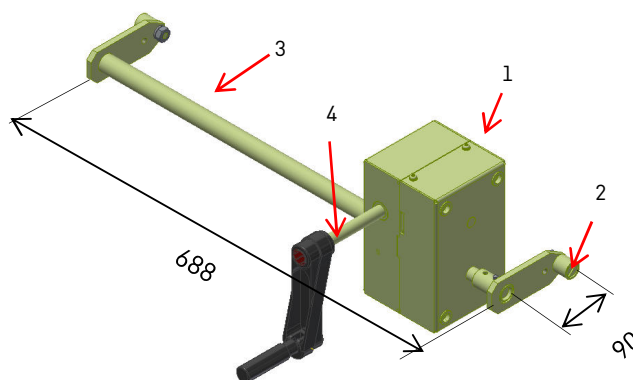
Схема узла блокировки и редукции ВЭ К-37.
